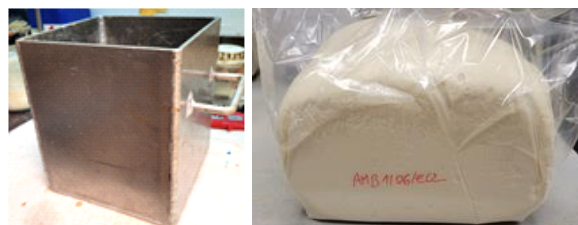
Molde de fabricación a expansión libre (izq.) y ejemplo de probeta obtenida (der.).
